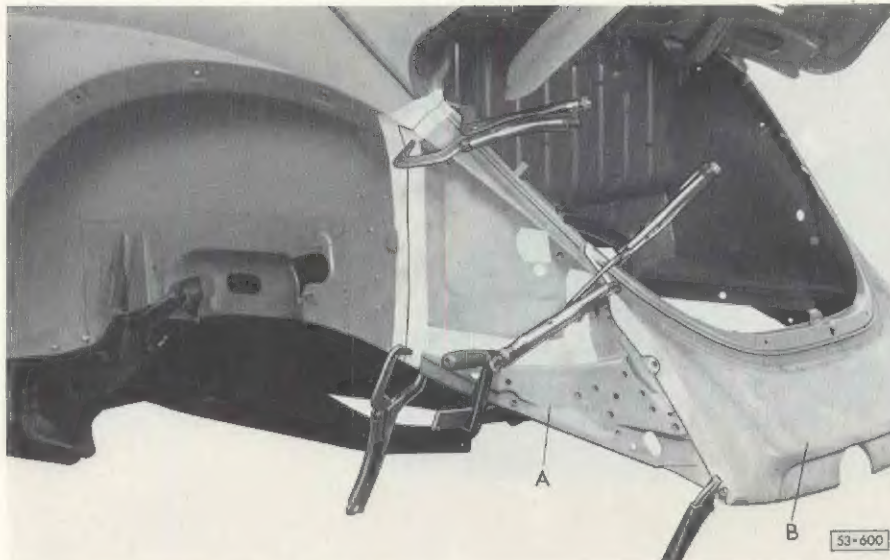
Seitenteil-Abschnittsteil, Motorabdeckblech und Abschlußblech hinten anpassen und anklemmen. Anschließend an einigen Stellen heftschweißen.
